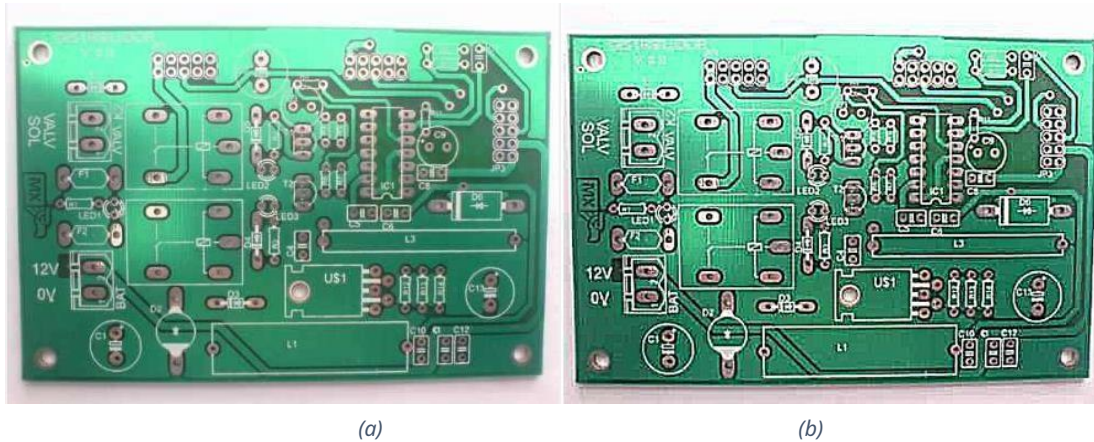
Imagen original de una PCB (a) contra imagen mejorada de una PCB (b).
